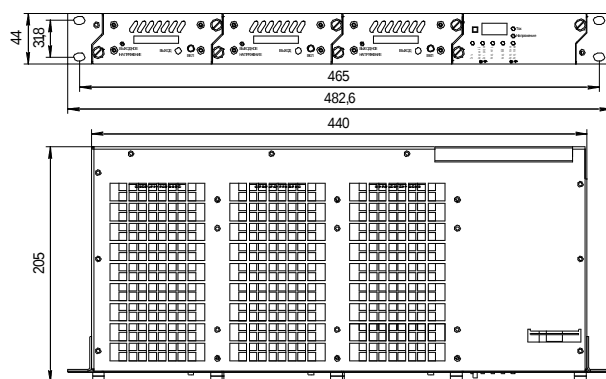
Габаритный чертеж УЭП-2К
